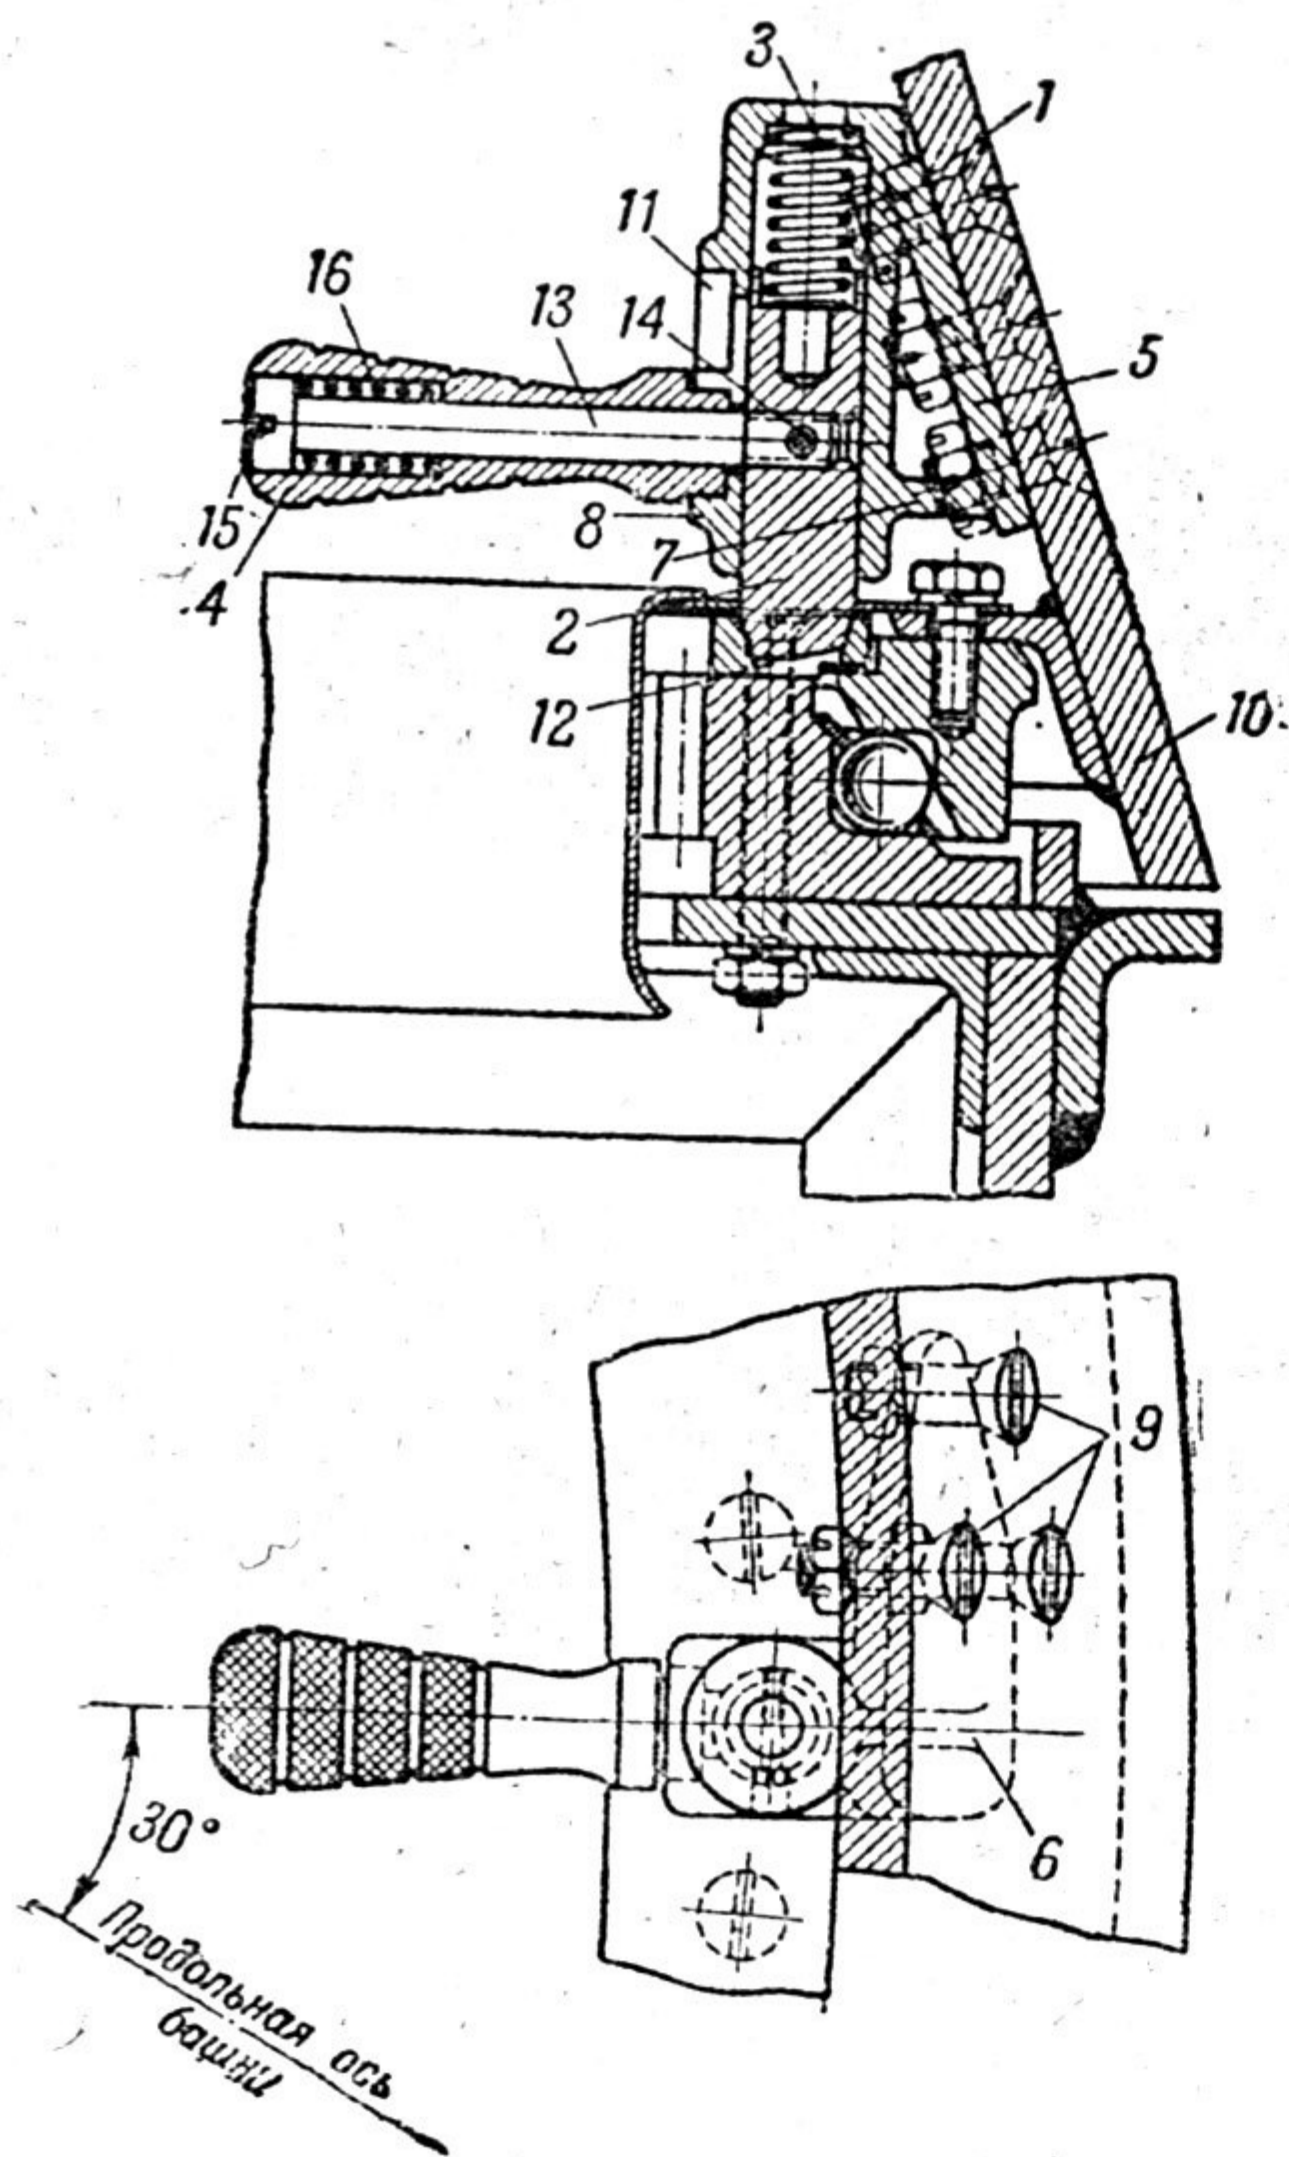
Стопор башни со сварным лобовым щитом:
